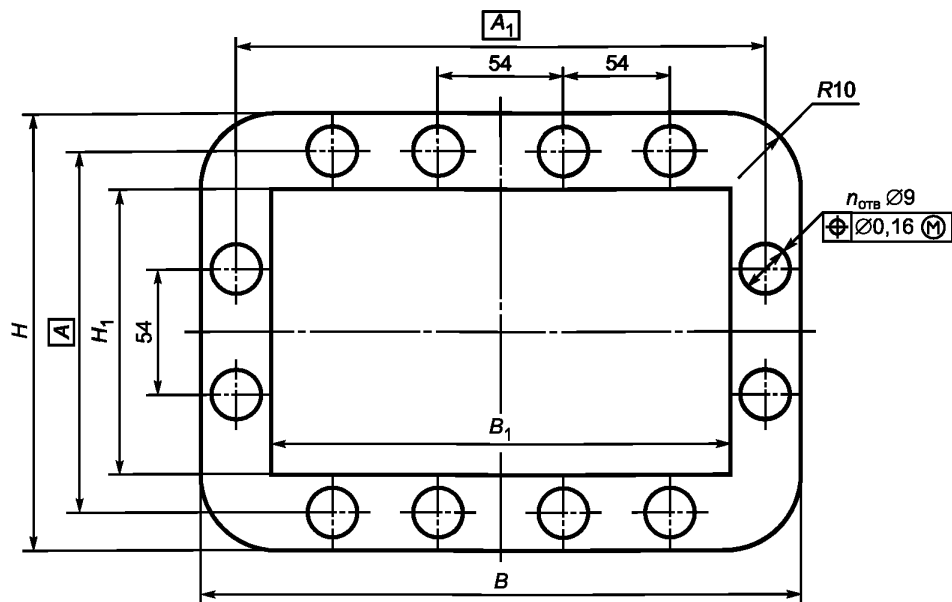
Присоединительные размеры прямоугольных фланцев с расположением четного количества отверстий по сторонам  $H$  и  $B$
